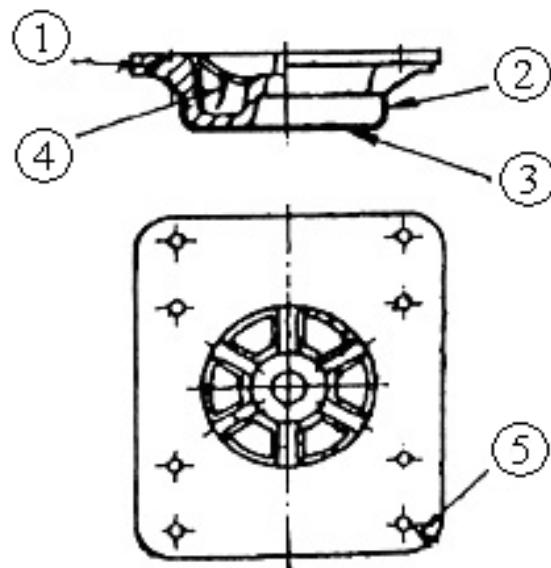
Дефекты пятника, ремонтируемые сваркой или наплавкой
